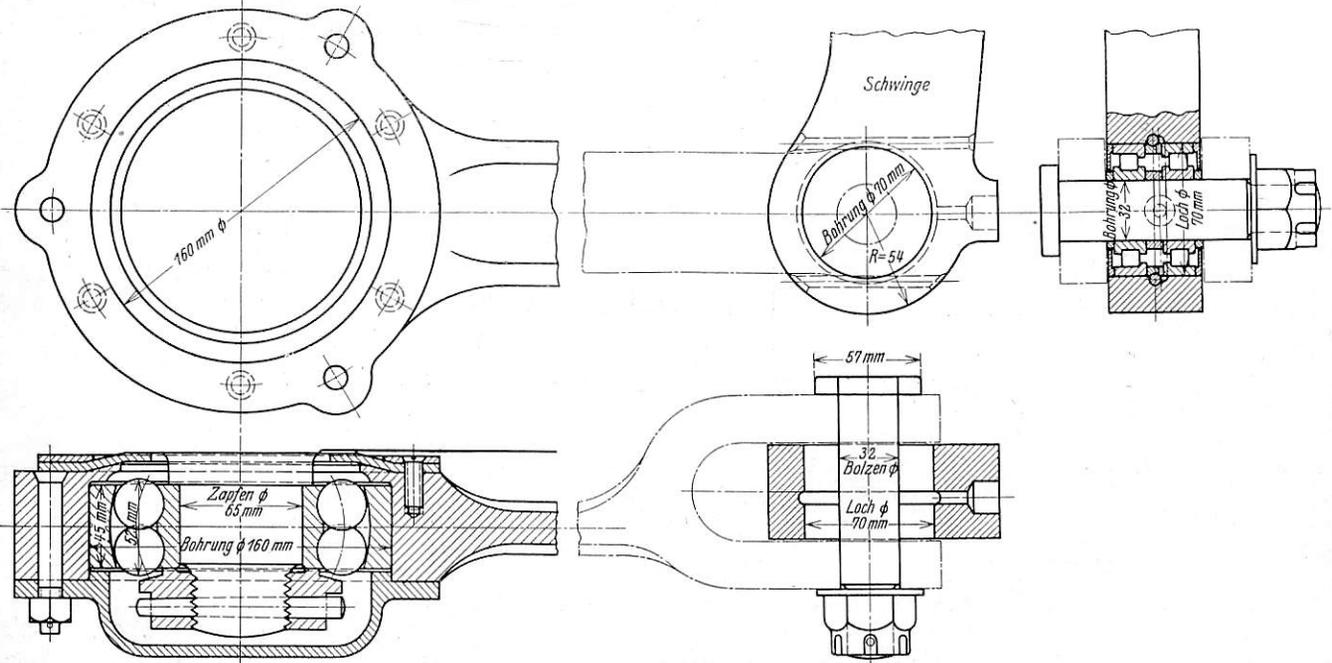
Schwingen-Antriebsstange mit Kugel- und Rollenlagern.
